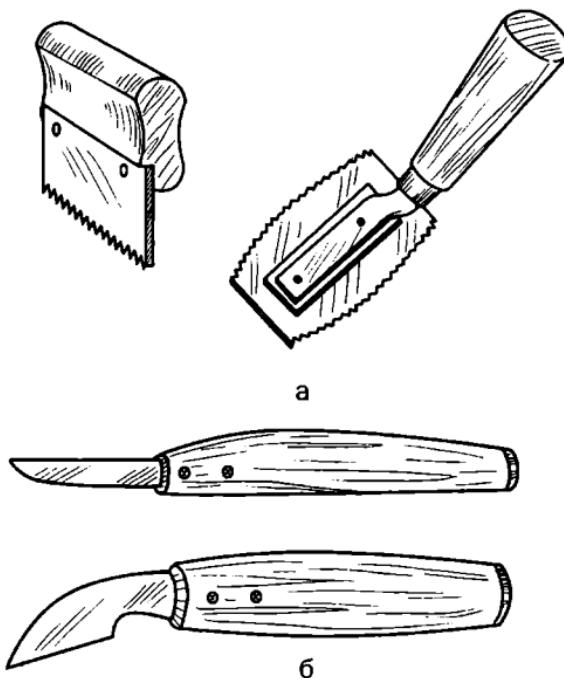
Инструмент для раскройки шпона: а — ножи-пилы; б — ножи-резаки
